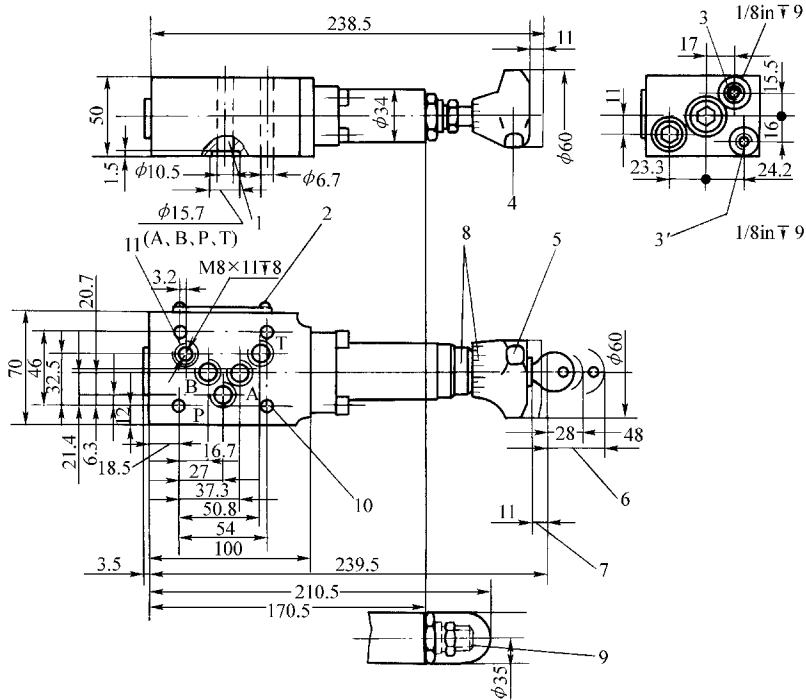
ZDR10DA 及 ZDR10DP 型外形尺寸
